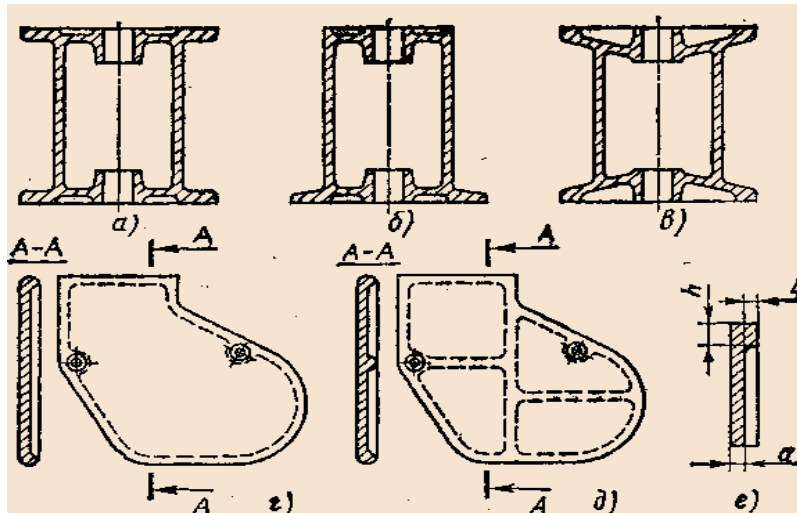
Конструкция литых деталей, снижающих усадочные напряжения в отливках
